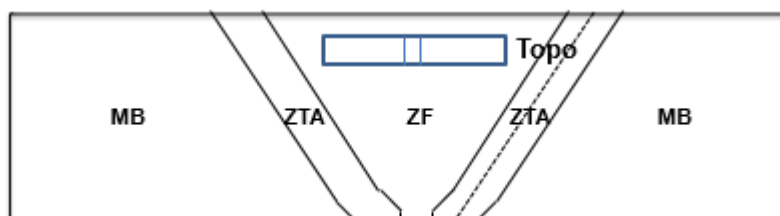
Representação esquemática de uma junta soldada com direção do entalhe para teste Charpy na ZF.
